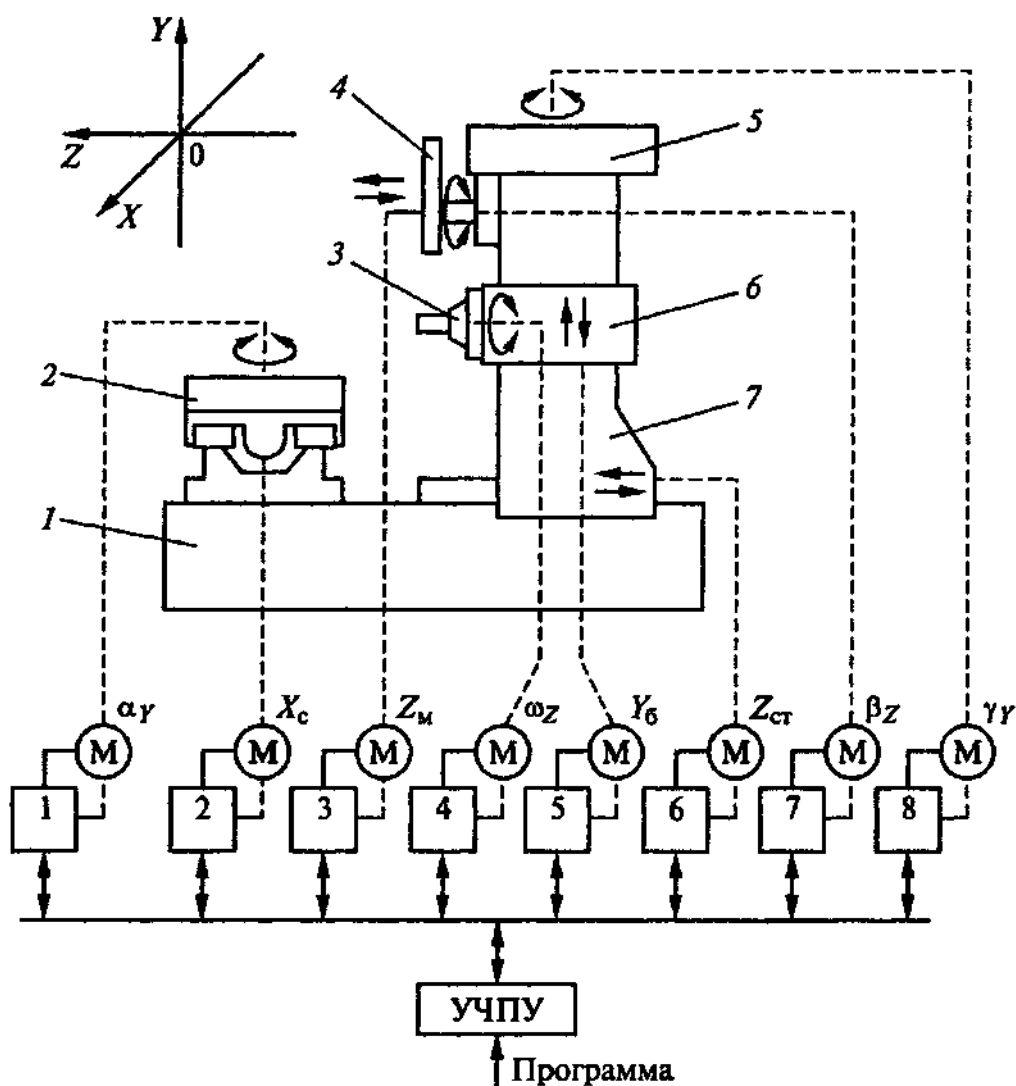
Многооперационный сверлильно-фрезерно-расточной станок с горизонтальным шпинделем
